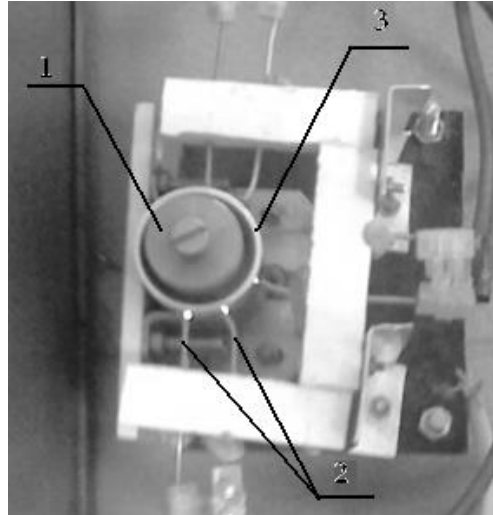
Приспособление для искрового упрочнения образцов
